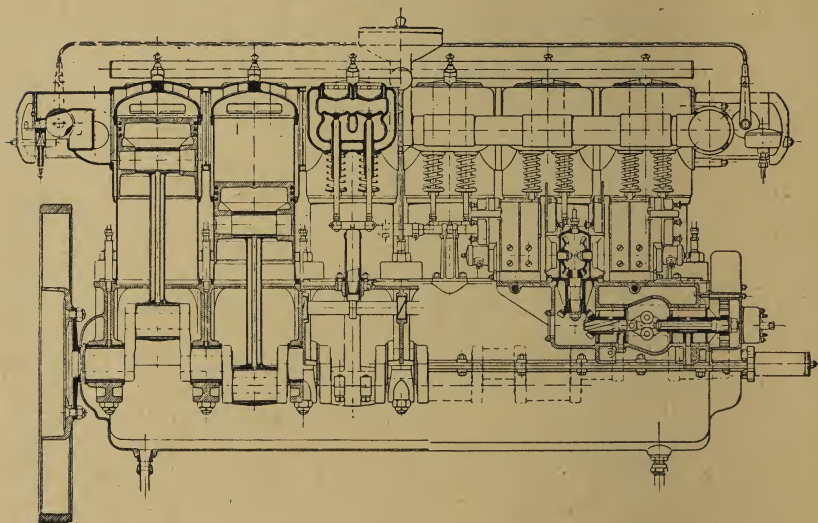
Längsschnitt des Maybach-Luftschiff-Motors.
